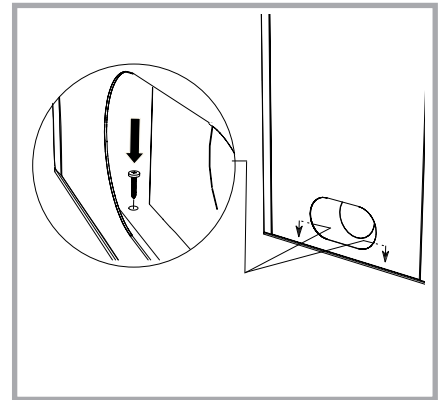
Fixierung des Kaminofens mittels Schrauben.
